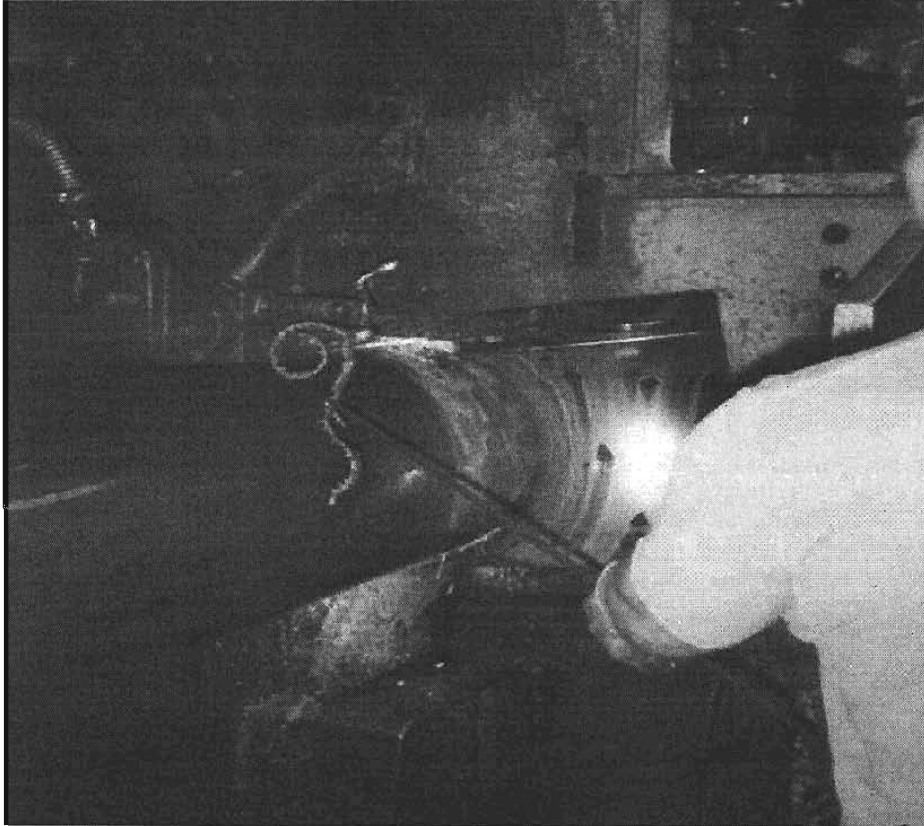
Retiro de acero soldado que pudiera hacer borde en la línea de soldar.
